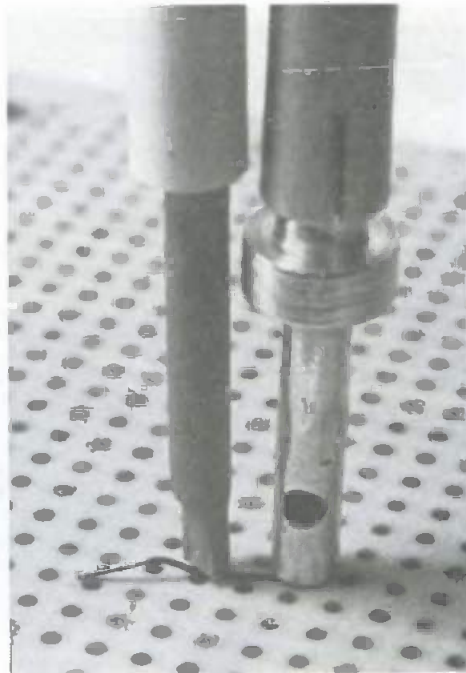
Il faut bloquer le fil d'amorce avant de bobiner. Le trou latéral sert à compter 6 à 8 tours.
